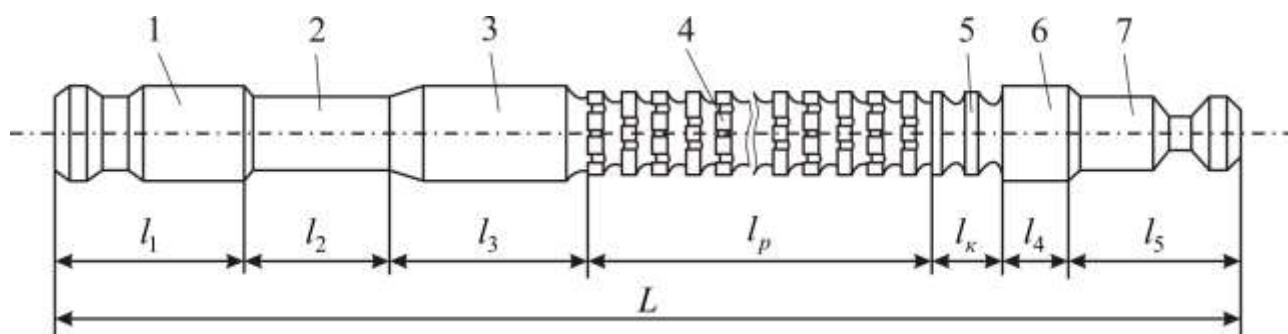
Конструктивные элементы протяжки для обработки отверстий:
